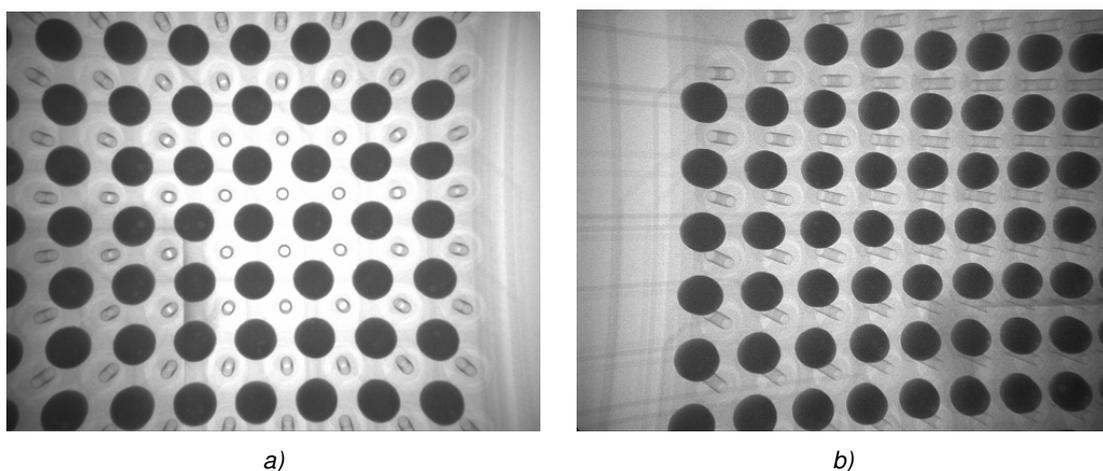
Radiographie des billes du BGA montrant la régularité des formes des billes
